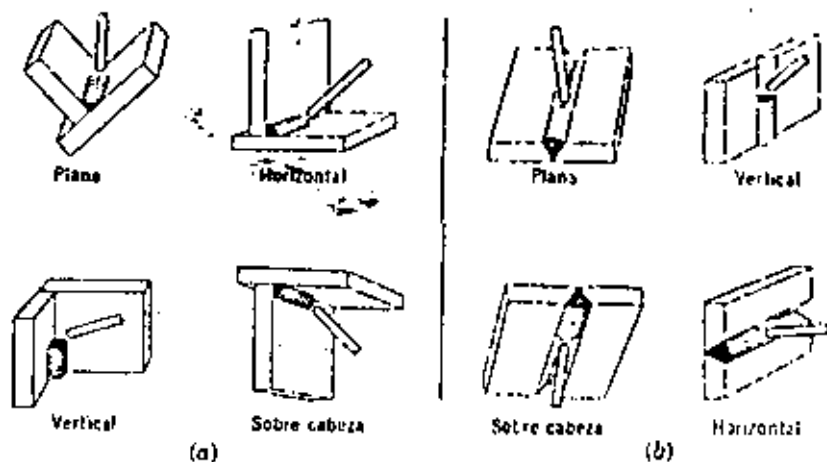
Posiciones para soldar: (a) soldaduras de filete, (b) soldaduras a tope.
